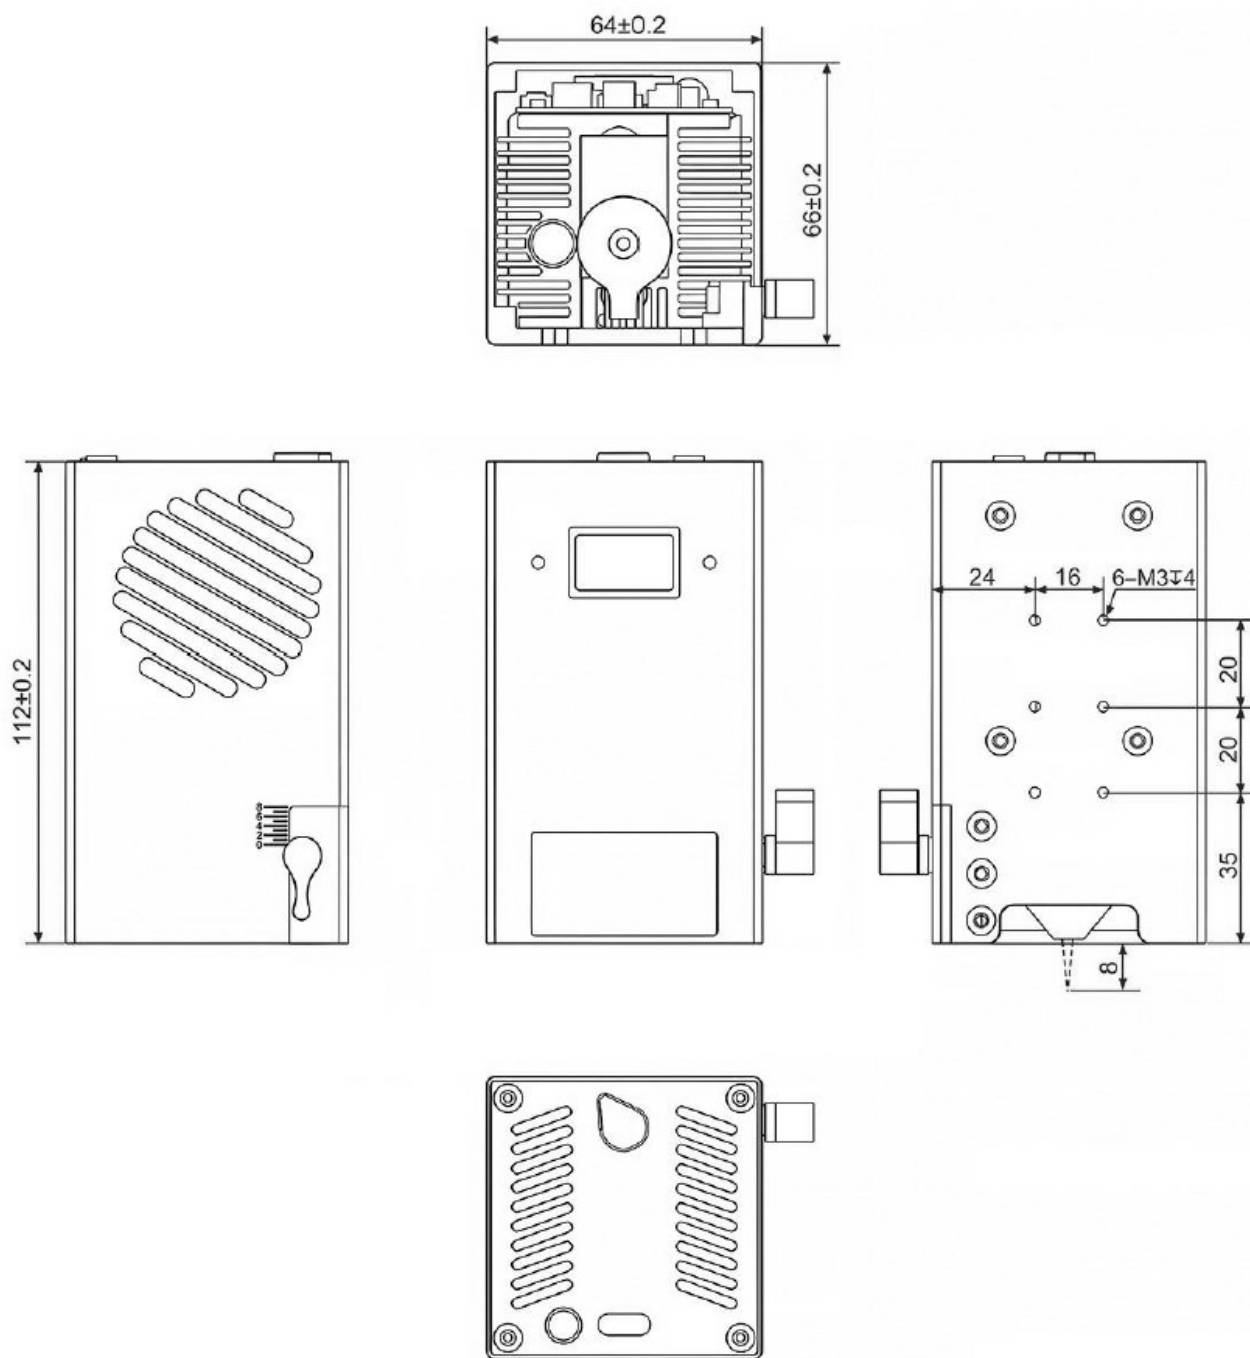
Габаритный чертеж лазерного модуля LT20W-24V.
